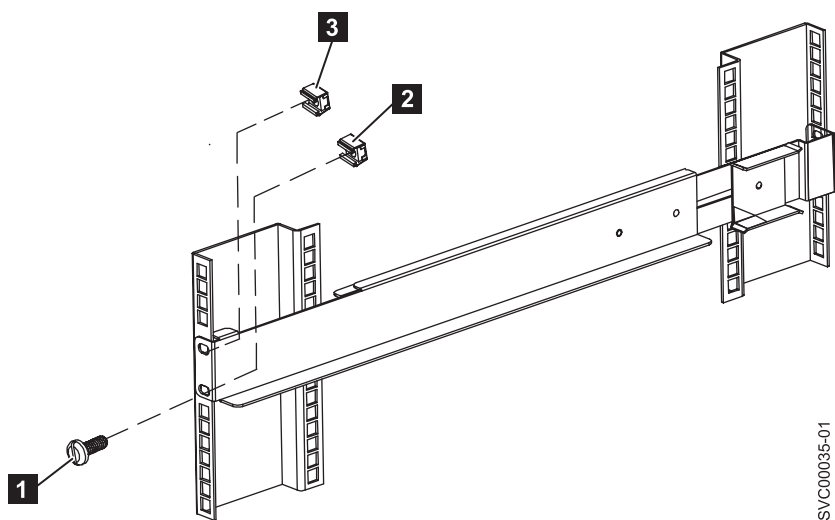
Removendo o trilho frontal no 2145 UPS-1U
